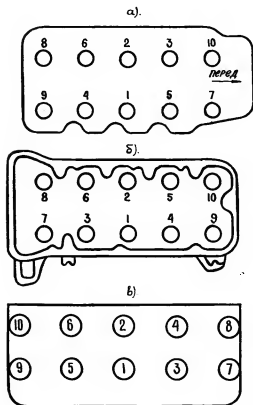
Последовательность затяжки гаек крепления головки блока цилиндров двигателей:
